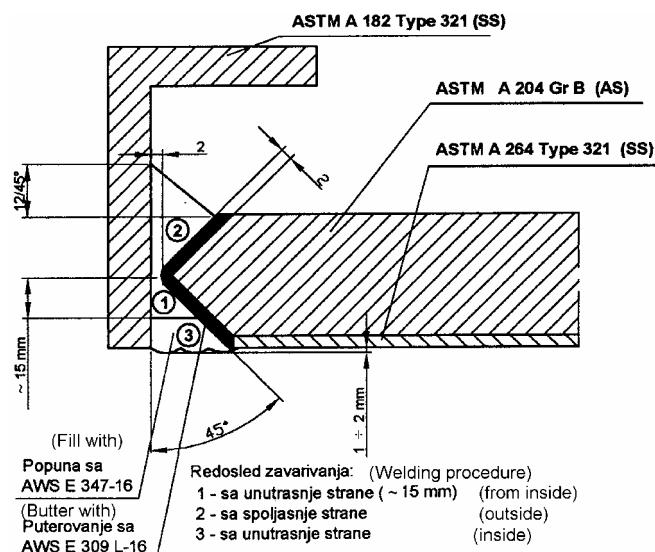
Kladiranje zavarivanjem, nakon brušenja deformisane zone kladinga sa unutrašnje strane.
